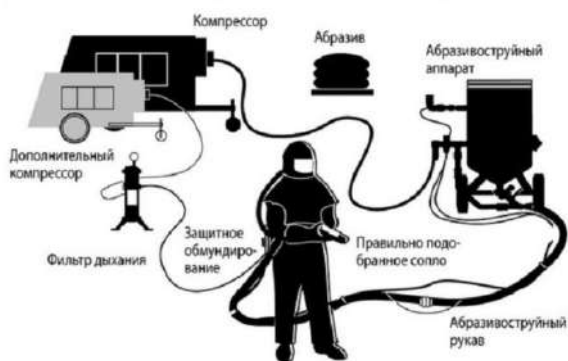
Оборудование для дробеструйной очистки деталей
